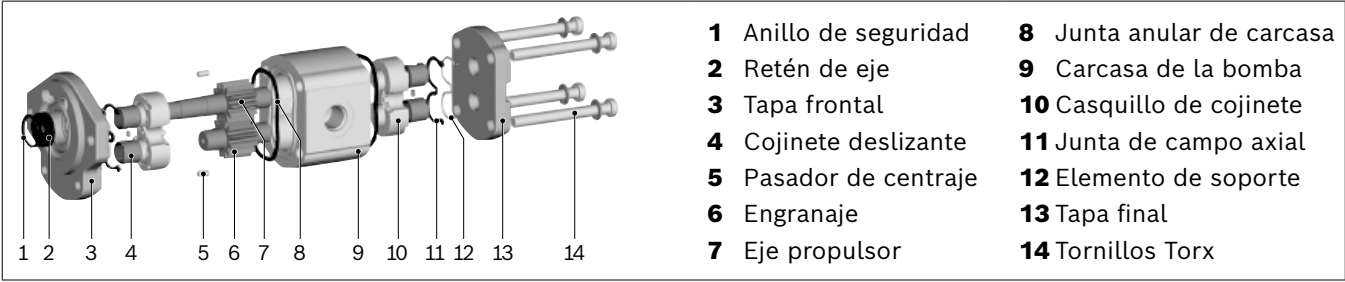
Estructura de la bomba a engranajes con dentado exterior
